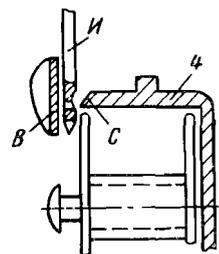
Положение иглы и шпулки в челноке машины 22-А класса
